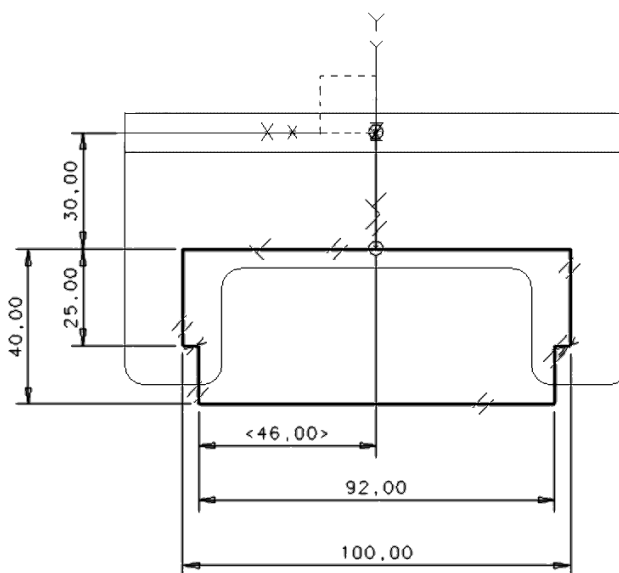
Skica výstupku 130x130x5 mm v horní části příruby
